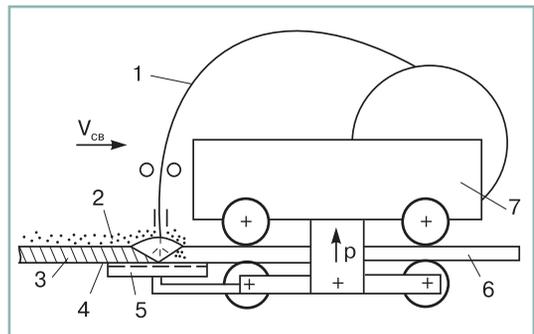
Схема односторонней автоматической сварки с ползуну, жестко связанном с автоматом: 1 — сварочная проволока; 2 — флюс; 3 — шов; 4 — шлак; 5 — медный ползун; 6 — основной металл; 7 — сварочный автомат
